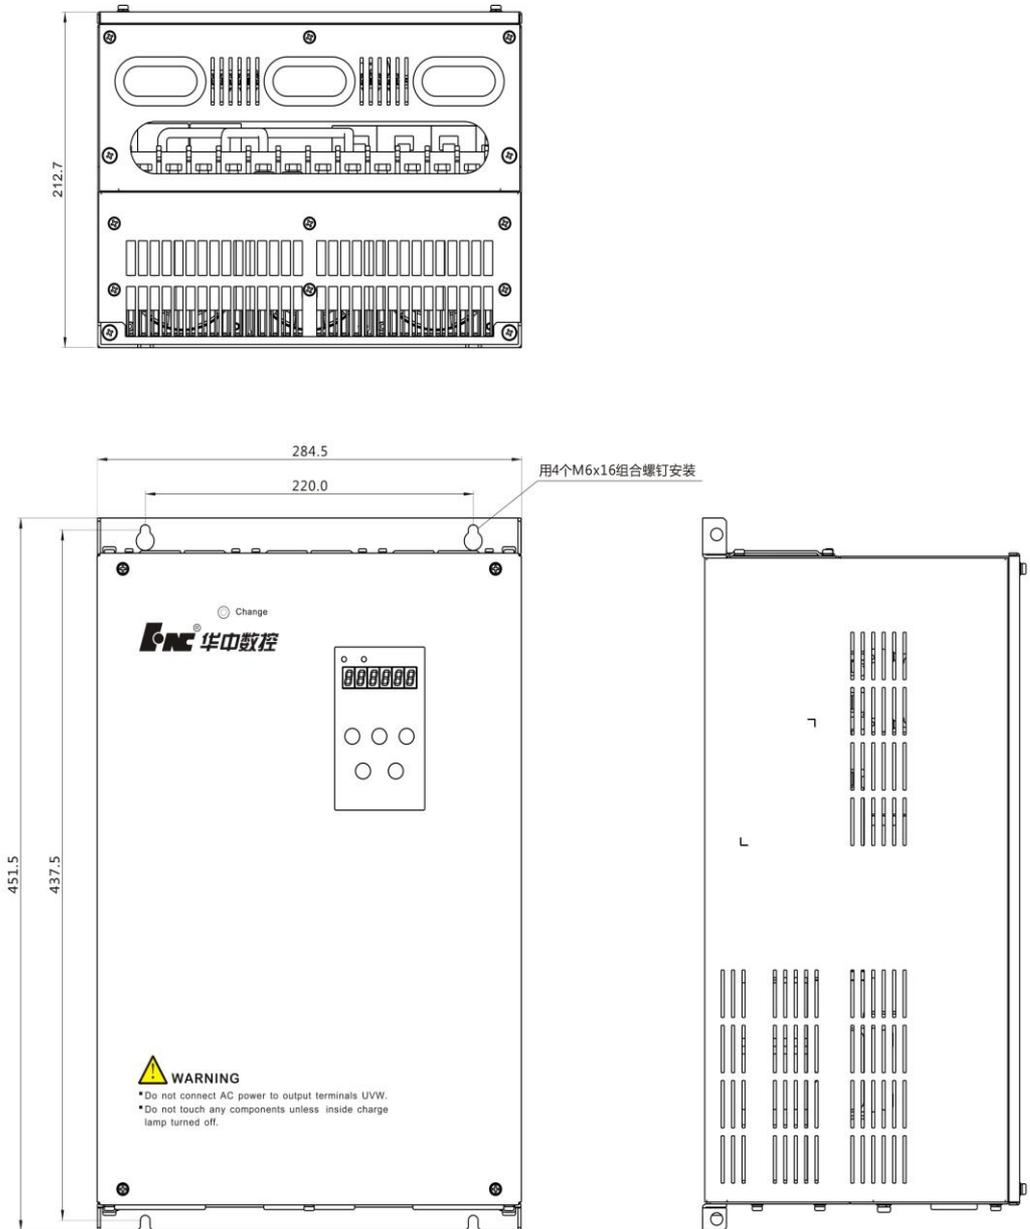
HSV-180U1S-100, 150 主轴驱动单元外形尺寸（带辅助安装装置 单位：mm）
